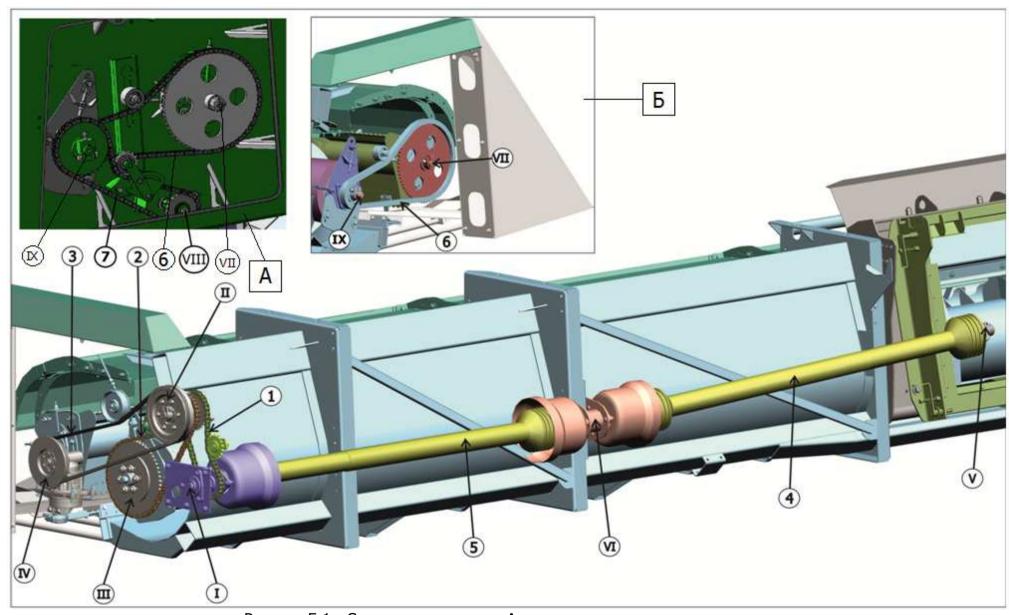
Схема передач жаткиА – жатка с протягивающим валом;
